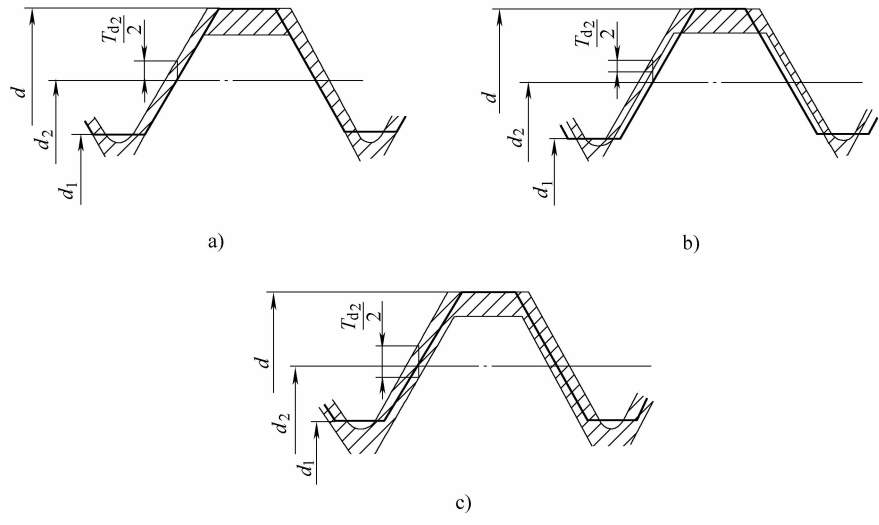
过渡配合螺纹外螺纹公差带
